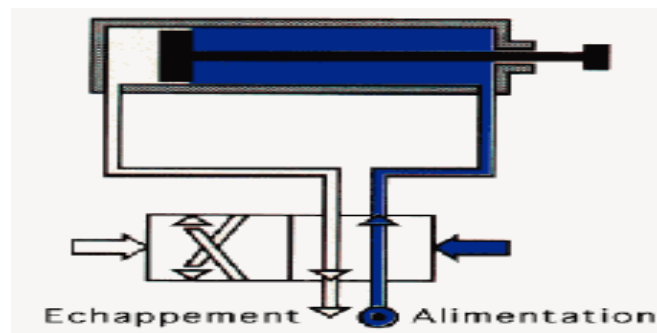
Vue en coupe d'un vérin pneumatique.
